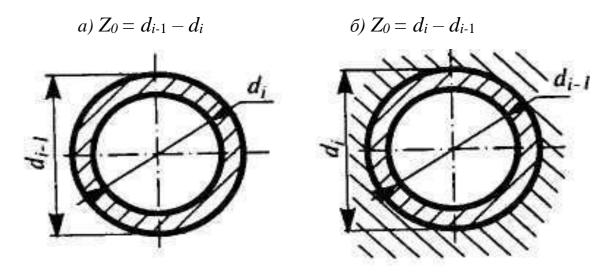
Схемы расположения припусков для наружной (a) и внутренней (δ) поверхностей
